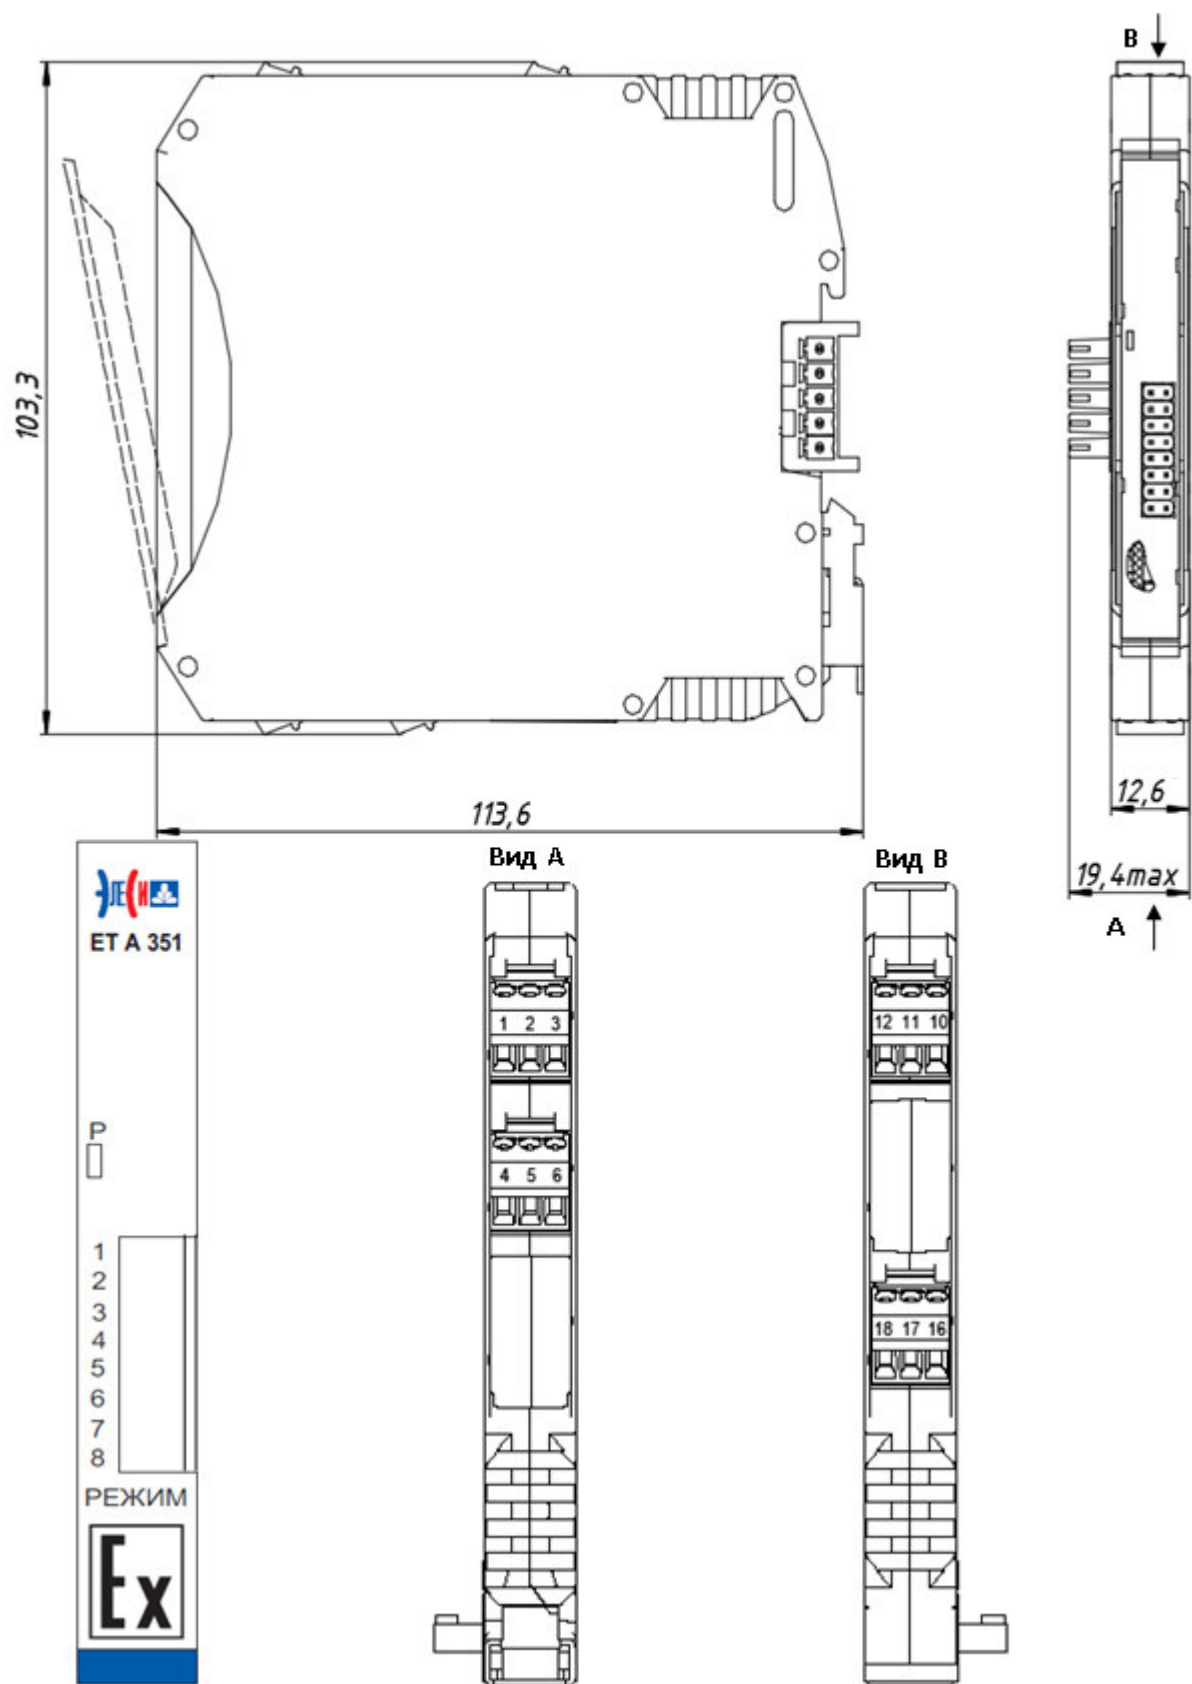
Габаритный чертеж и внешний вид барьера искрозащиты ET A 351
